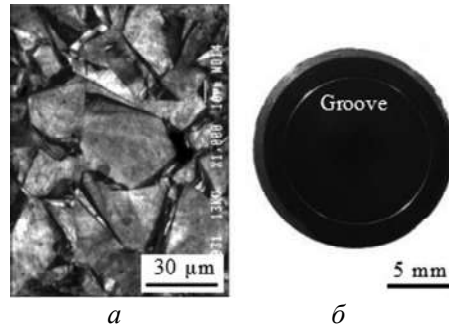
Стан поверхні (а) CVD алмазного диска (б) для шліфування [46].
